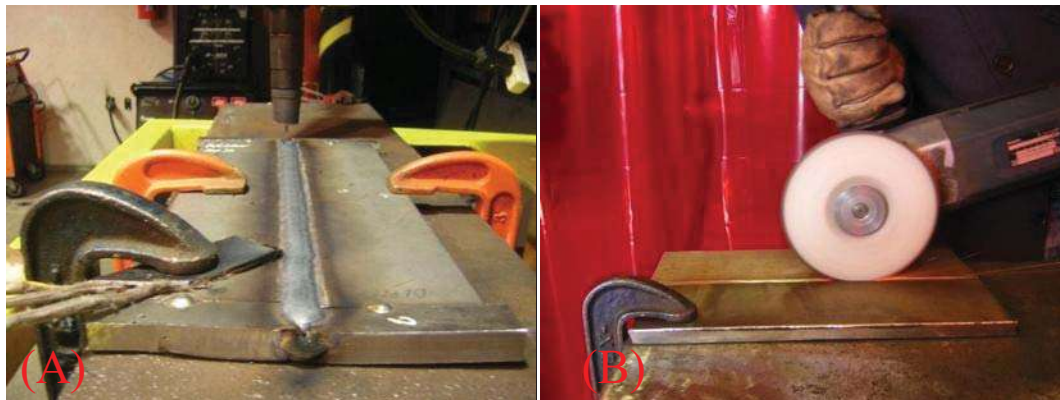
9 (A) Primer cordón de soldadura (B) Limpieza de raíz del primen cordón de soldadura.
